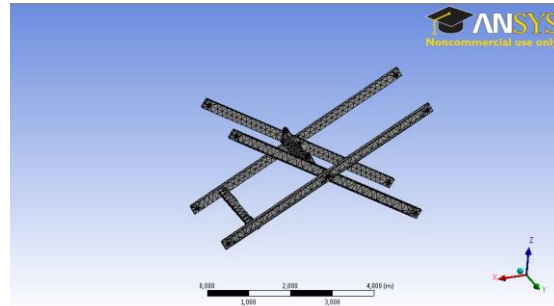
Modelo y mallado de las tijeras elevadas
